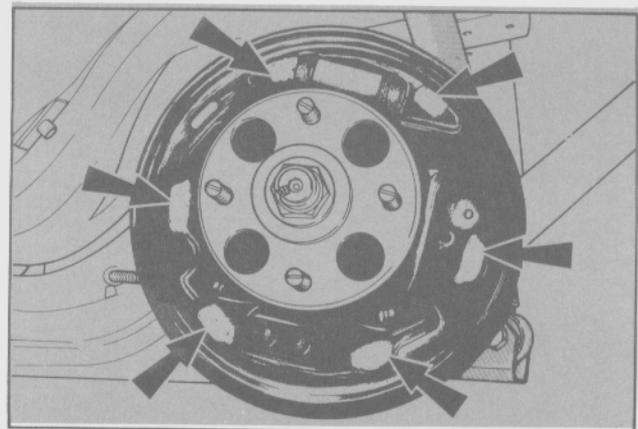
Punto de contacto de las zapatas en el plato de anclaje
